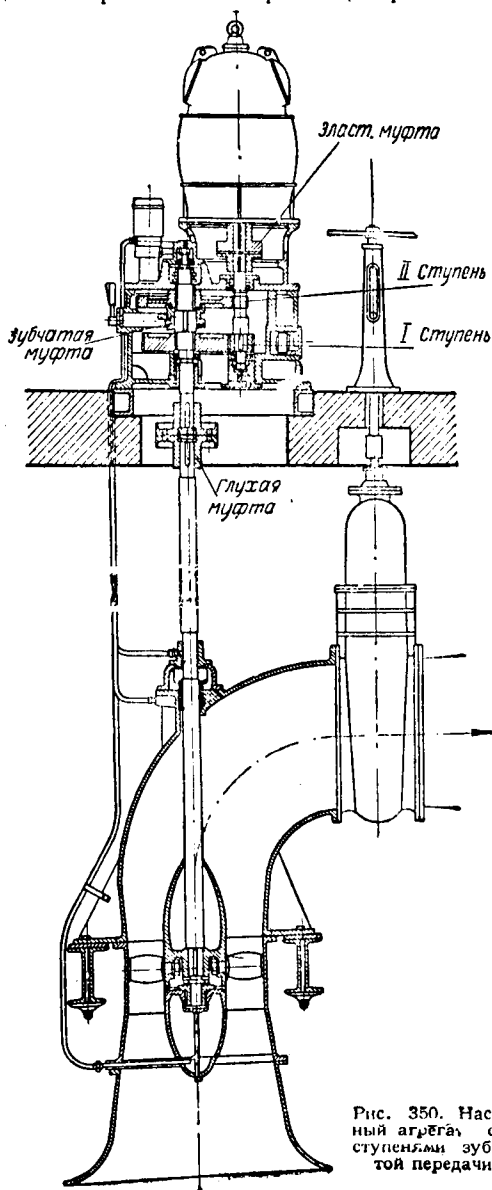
Насосный агрегат с 2 ступенями зубчатой передачи.
